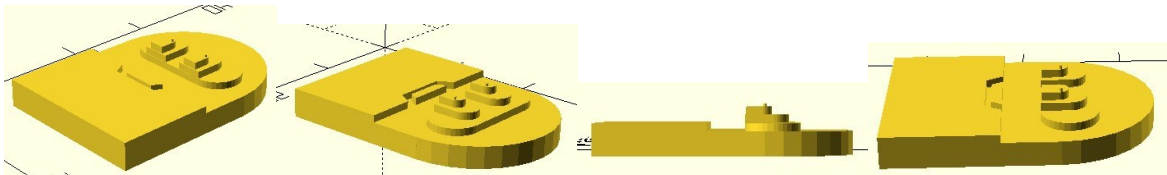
Spodní část těla, Obr. 35 – Půlka těla
